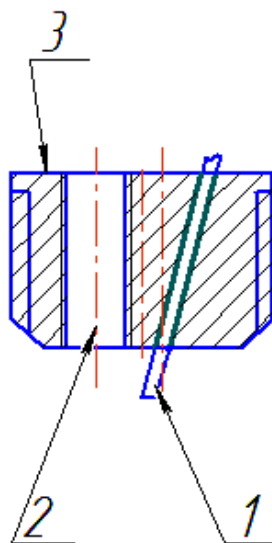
Схема ИД у свечи зажигания: 1 – ИЗ; 2 – отверстие под свечу зажигания; 3 – корпус ИД.
